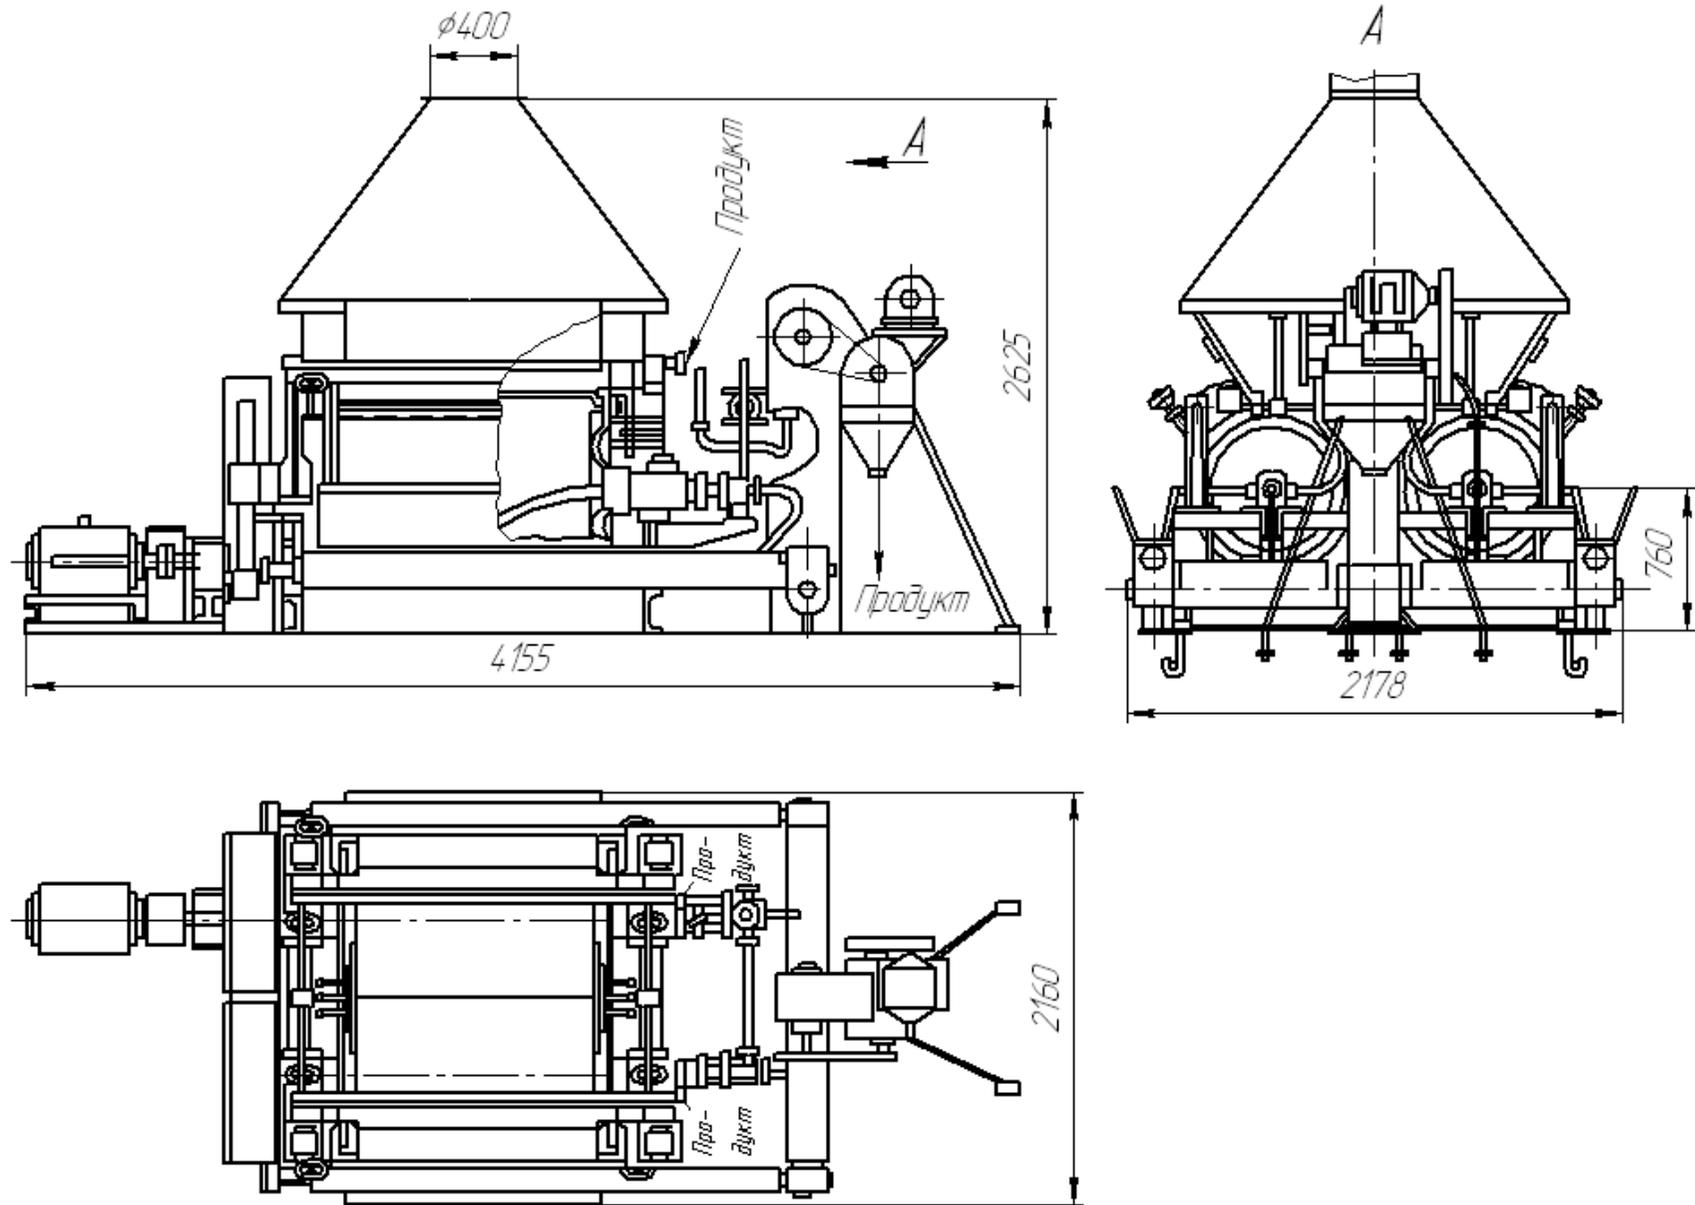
Сушильно-дробильный агрегат СДА-250
